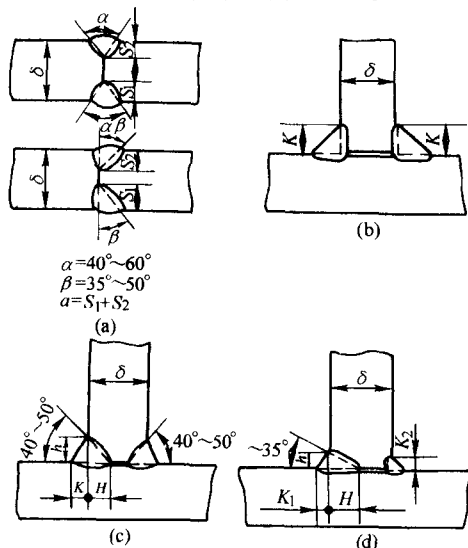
厚板部分熔透的焊接接头设计
